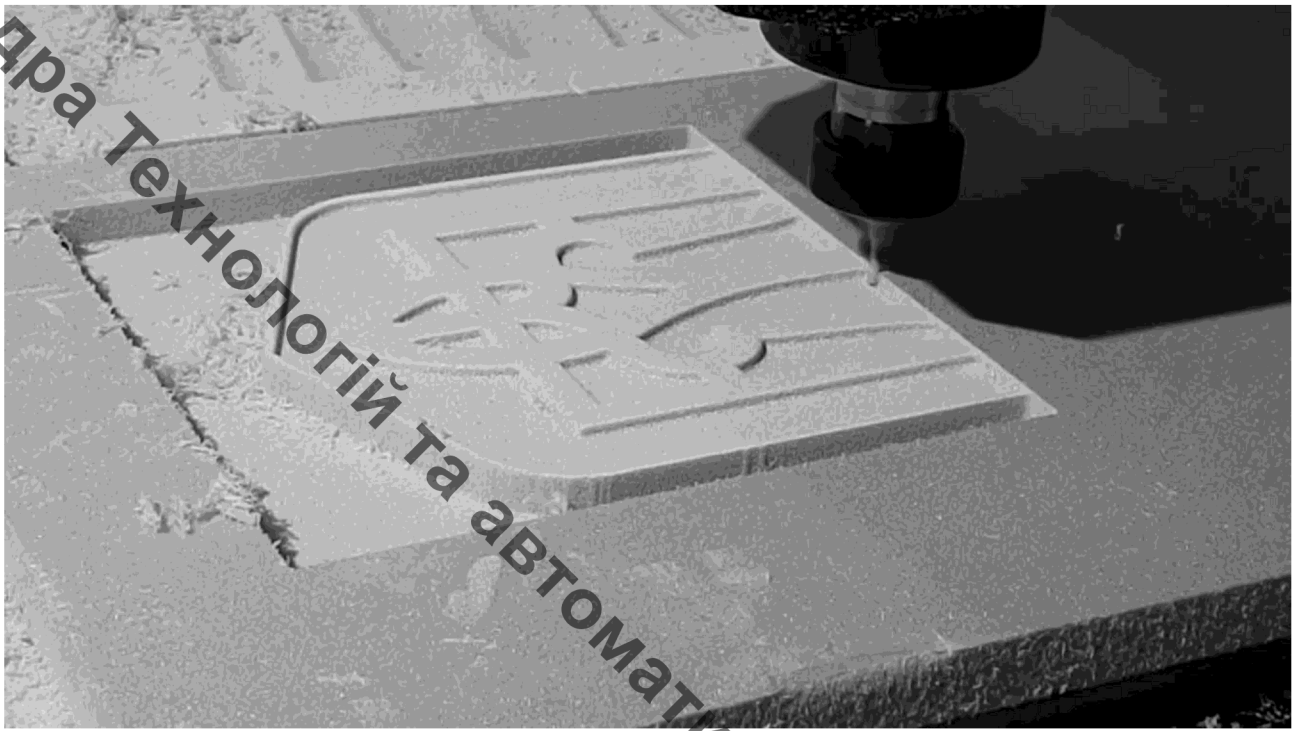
Обробка пінопласту на фрезерно-гравірувальному верстаті з ЧПК
